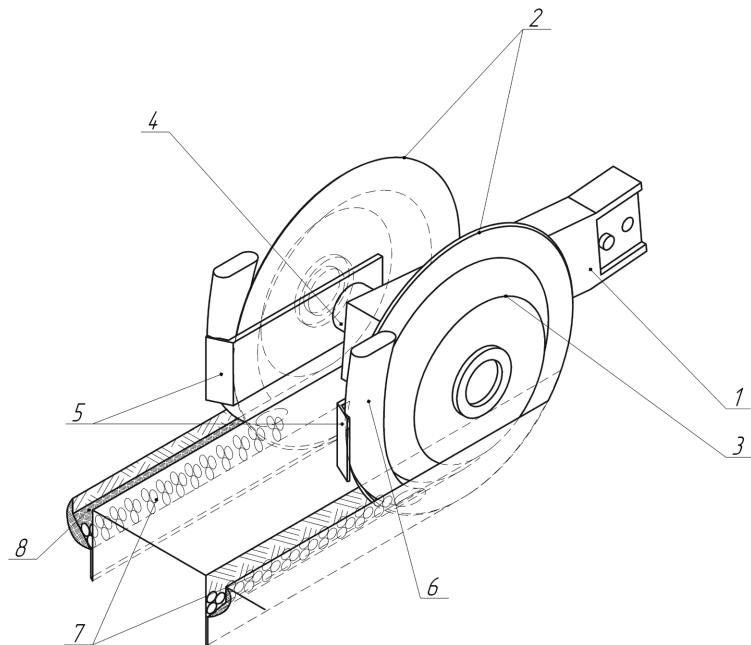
Технологическая схема двухдискового сошника с внешними симметричными усеченно-конусными ребордами и нулевым углом атаки дисков: 1 – корпус; 2 – диск; 3 – реборда; 4 – ось; 5 – пластина; 6 – семя направитель; 7 – семена; 8 – бороздка
